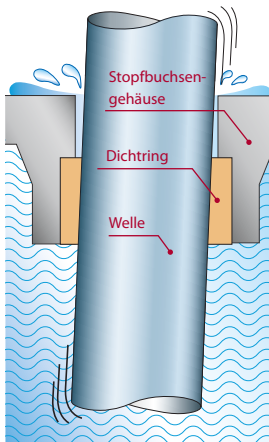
Geflochtene Stopfbuchsenpackung mit Gehäuse
